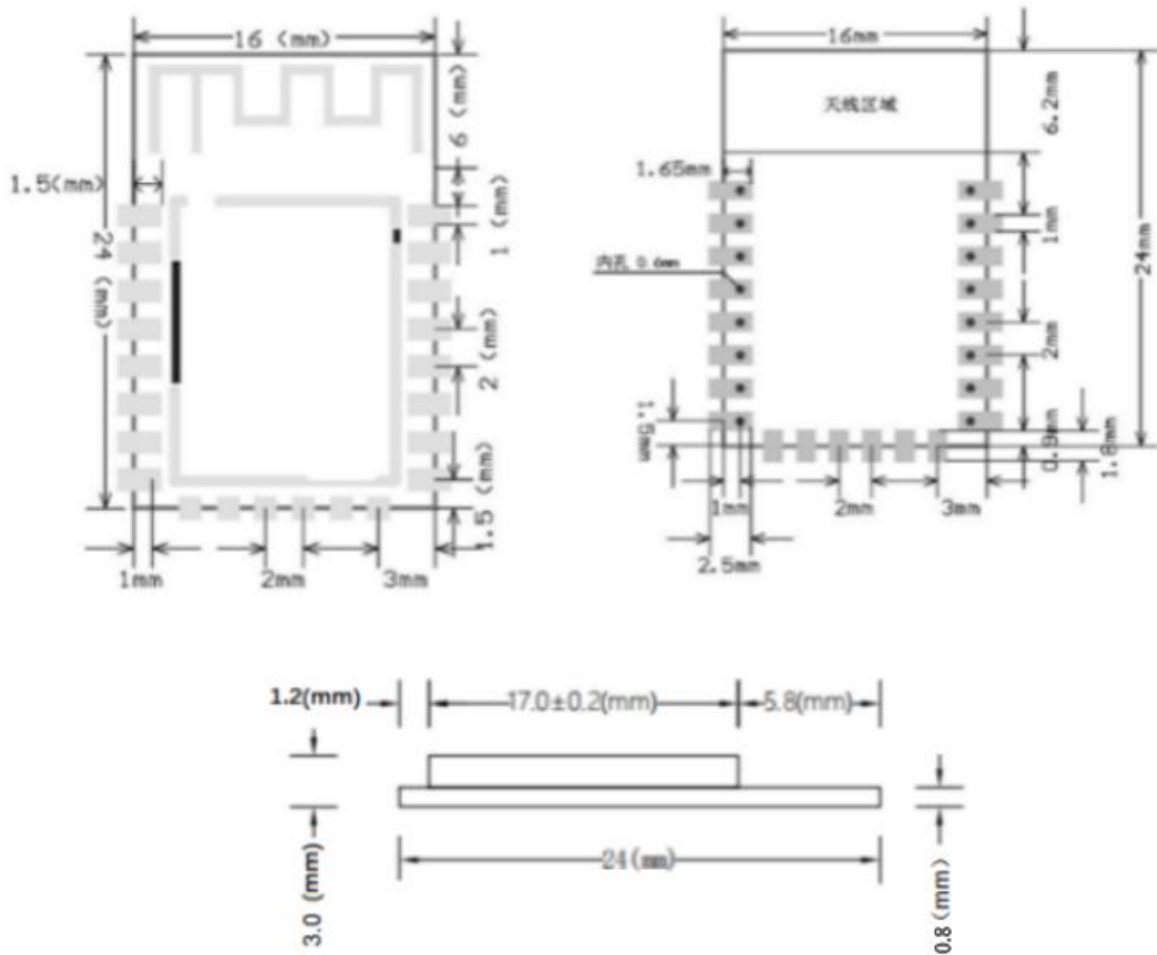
WG236-A 参考 PCB 封装/Recommend PCB Footprint
